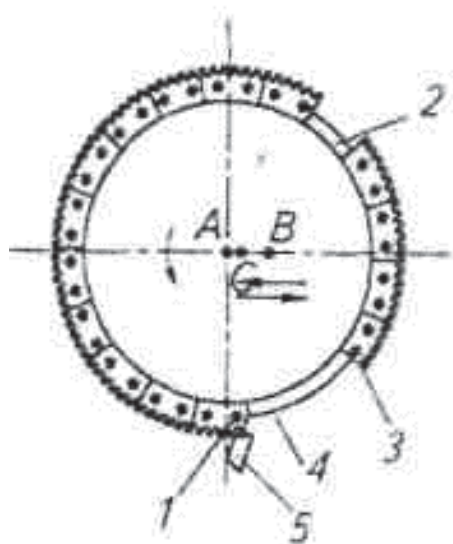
Схема кругового протягивания зубьев конического колеса: 1 – черновые резцы; 2, 4 – участки без зубьев; 3 – чистовые зубья; 5 – заготовка
